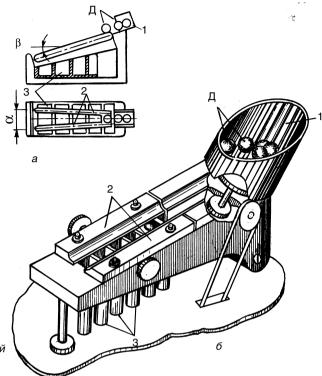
Контрольно-сортировочный автомат с клиновыми калибрами: а — схема; б — общий вид
